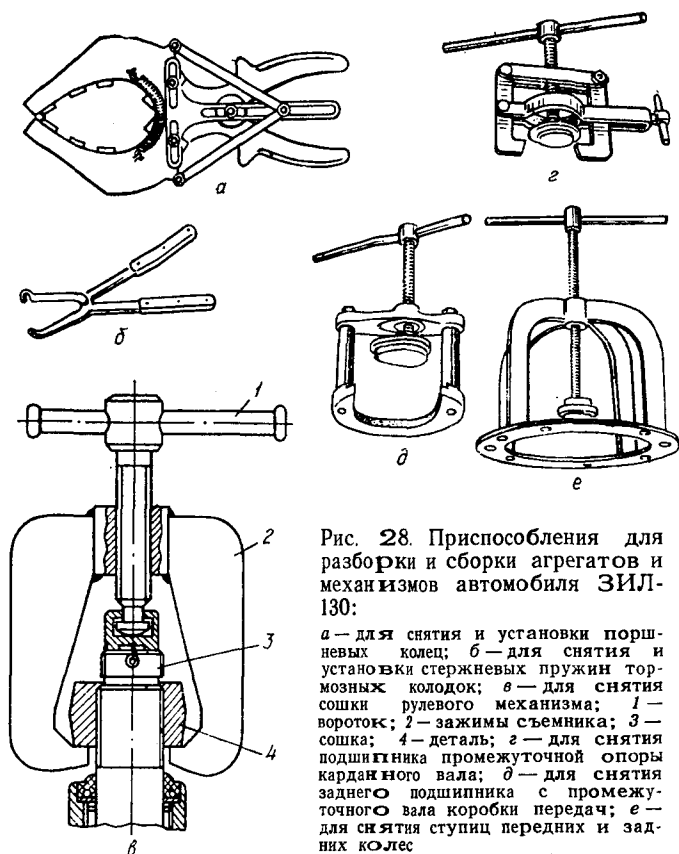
Приспособления для разборки и сборки агрегатов и механизмов автомобиля ЗИЛ-130:
